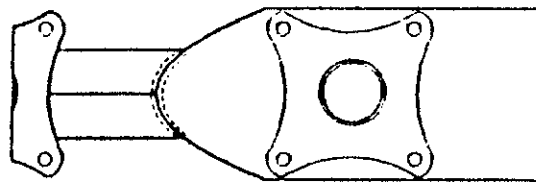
Контроль сварного шва накладок нижнего пояса продольной балки рамы
